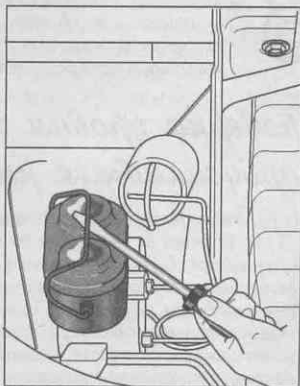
Снятие с помощью отвертки крышки металлического главного цилиндра
